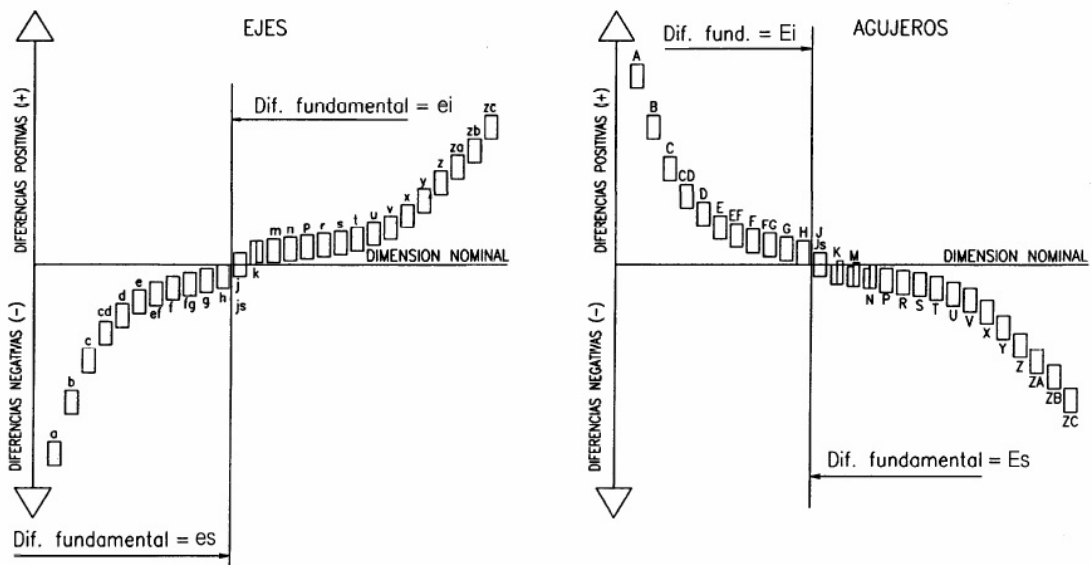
Posición tolerancias. Fuente: UNE-EN ISO 286-1.
